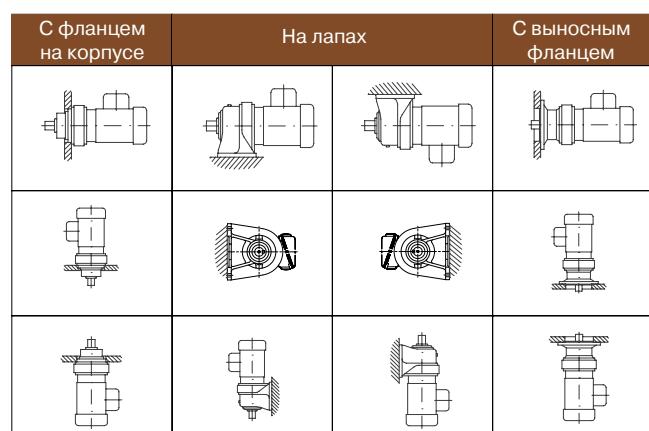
Конструктивные исполнения и способы монтажа планетарно-цевочных мотор-редукторов
